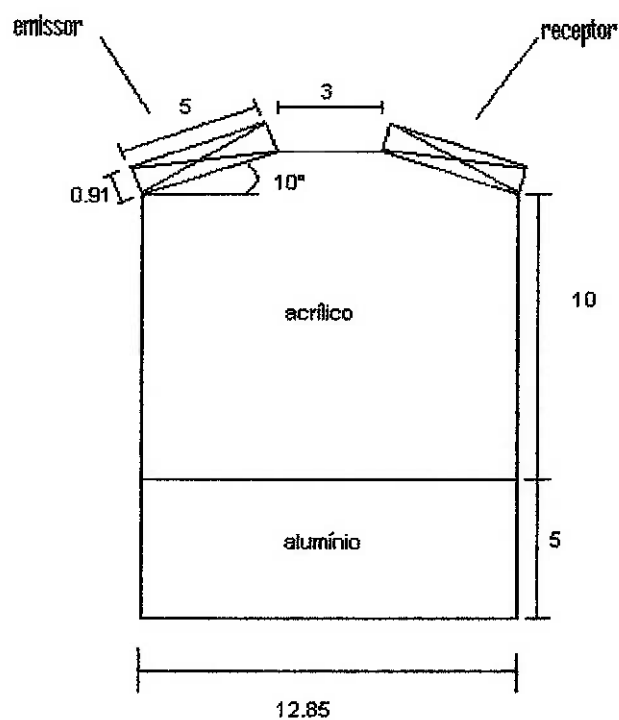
Dimensões do acrílico e ângulo de inclinação.
